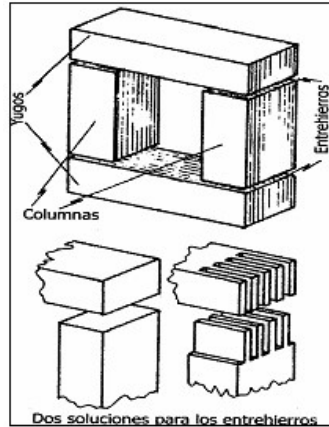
A. Armado de Núcleo con entre Hierros Planos y Dientes de Sierra
